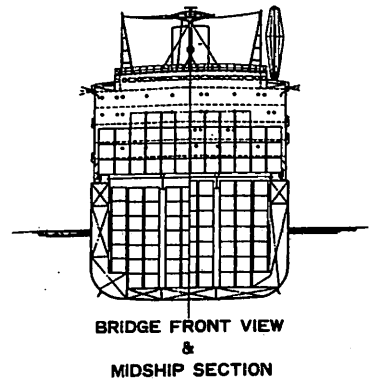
・1 M.S. "VERRAZANO BRIDGE" 一般配置図
